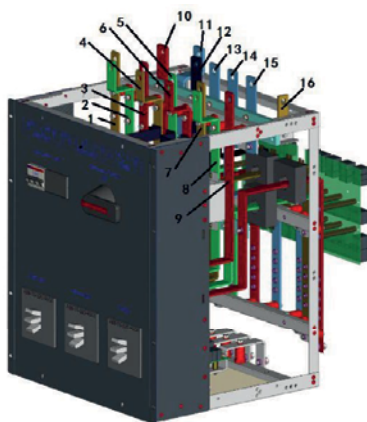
Верхняя схема электропроводки силового кабеля шкафа 200 кВА
